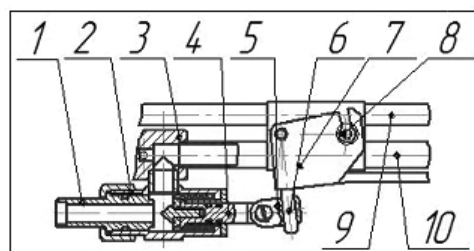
Модуль 4, третья группа: рычажный клапан с параллельным расположением корпуса и разомкнутой системой рычагов
